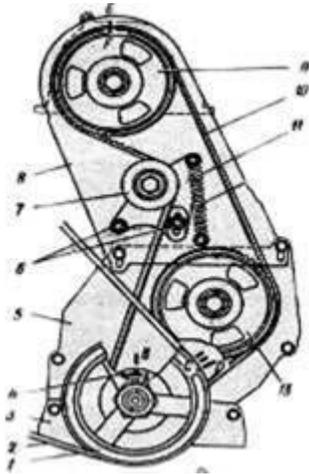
Схема приводу механізму газорозподілу двигуна ВАЗ – 2105:
